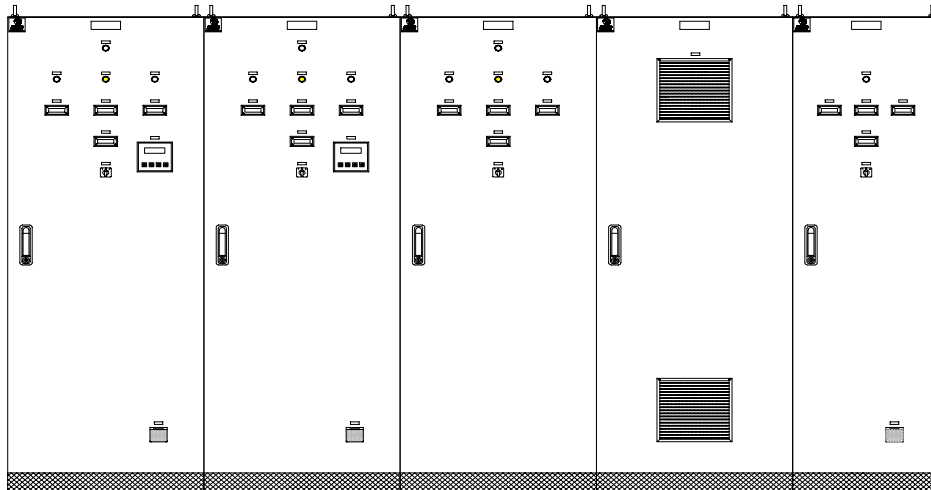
Vista externa de conjunto do tipo multi-colunas
